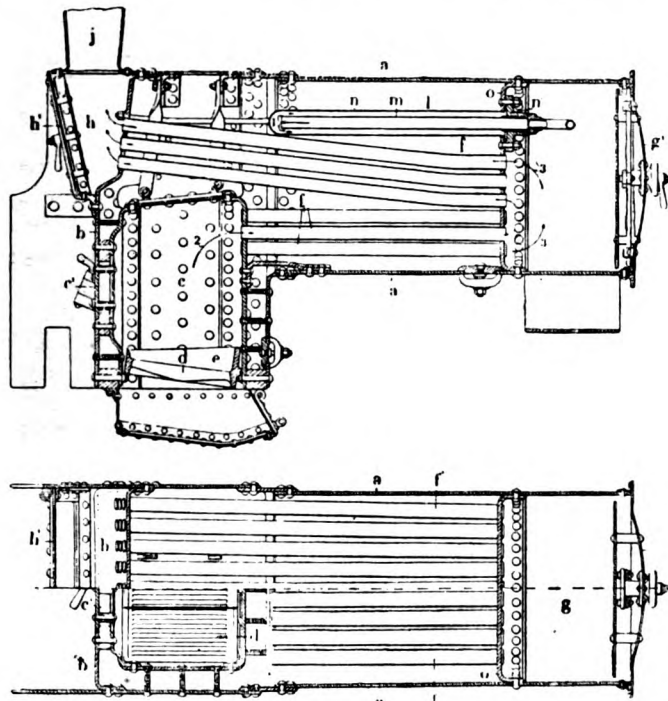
e 21. — Generatore tubolare Leroux — Sezione e pianta.
